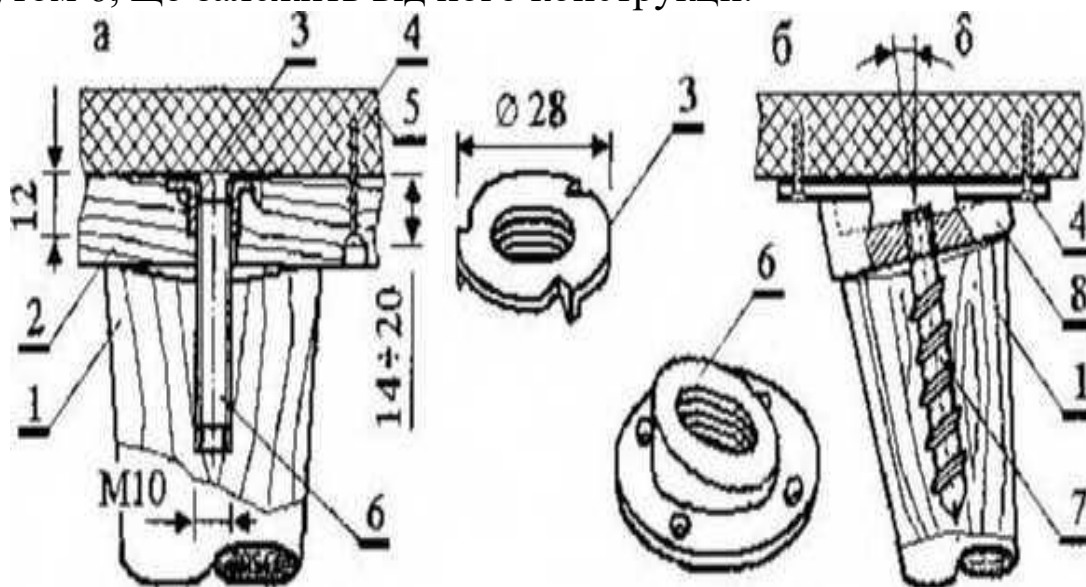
Кріплення підсадних ніжок (варіанти): а - штампованою гайкою, б - фланцем і шпилькою; 1 - ніжка, 2 - брусок жорсткості, 3 - штампована гайка-кліщ, 4 - шуруп, 5 - стінка корпусадолішня, 6 - шпилька з метричною різьбою, 7 - метрична шпилька-шуруп, 8 - фланець
